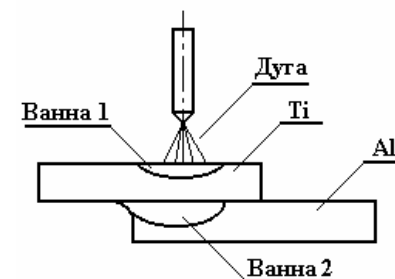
Схема решения задачи сварки титанового сплава с алюминиевым
